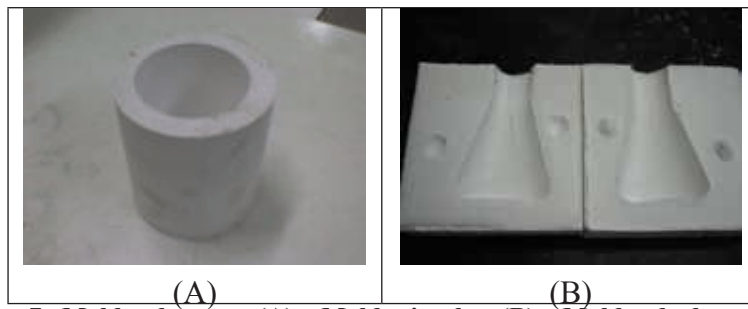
Moldes de gesso. (A) – Molde simples; (B) – Moldes de duas partes.
